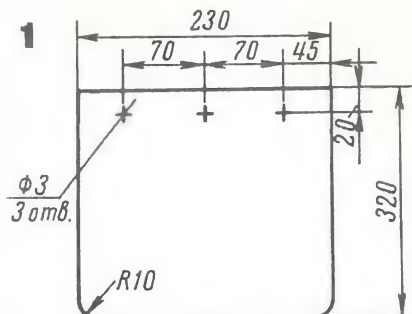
Заготовка из резины (толщина 5-6 мм).
